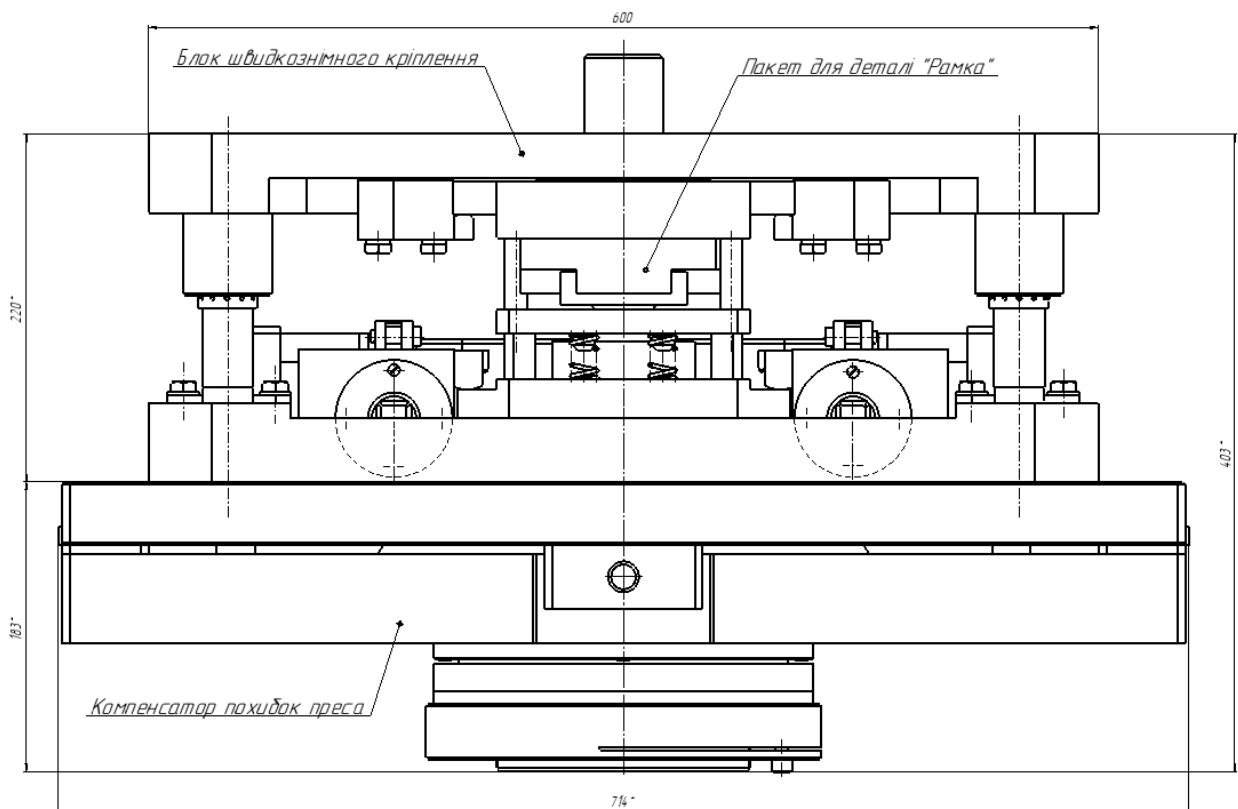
Компонувальний ескіз блока швидкознімного кріплення пакетів з компенсатором похибок преса і пакетом для штампування деталі «Рамка»
